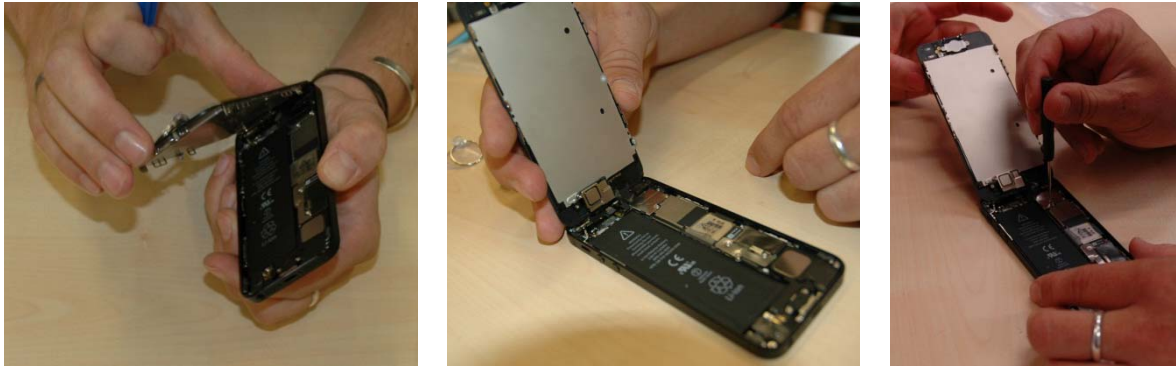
Geöffneter Gerätekorpus (links, Mitte); Lösen der Verschraubung zur Entfernung des Displays (rechts; 3x Kreuzschraube)
